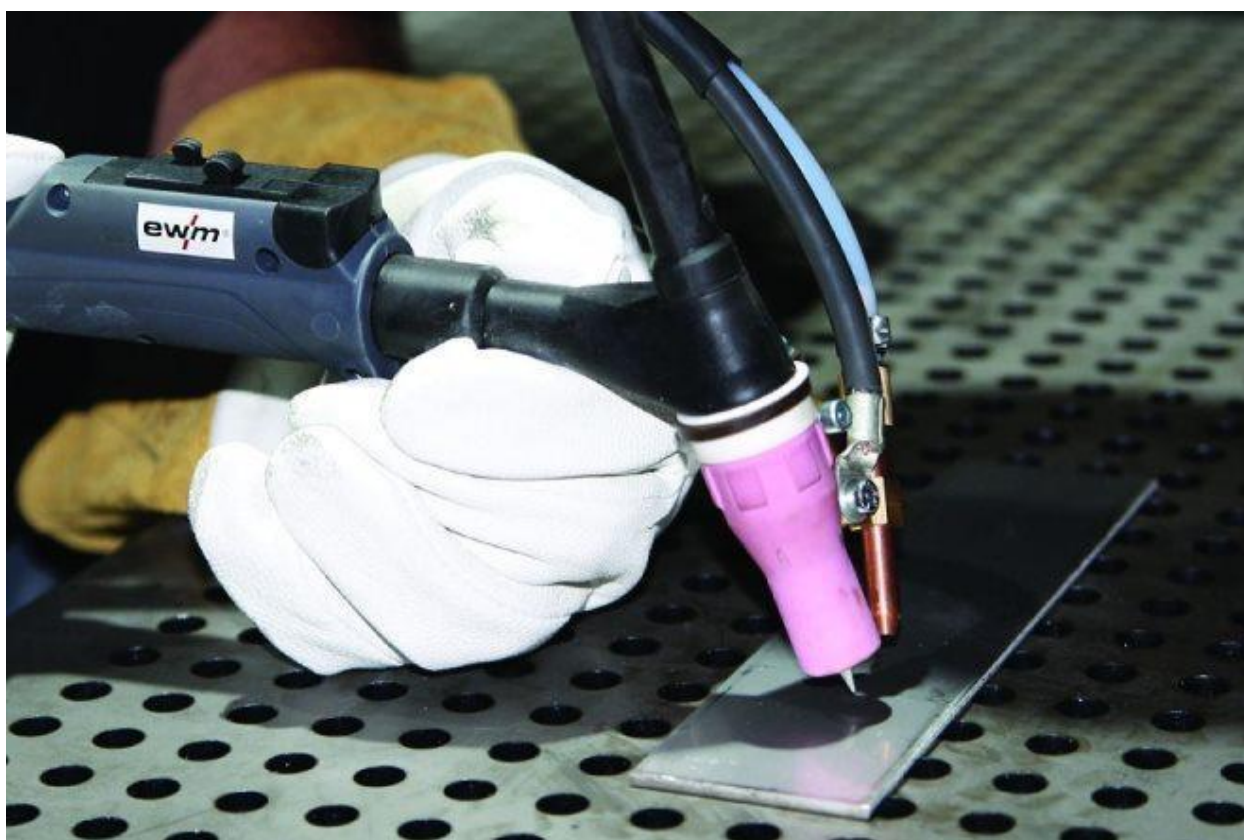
Горелка для сварки неплавящимся электродом при механизированной подаче присадки
